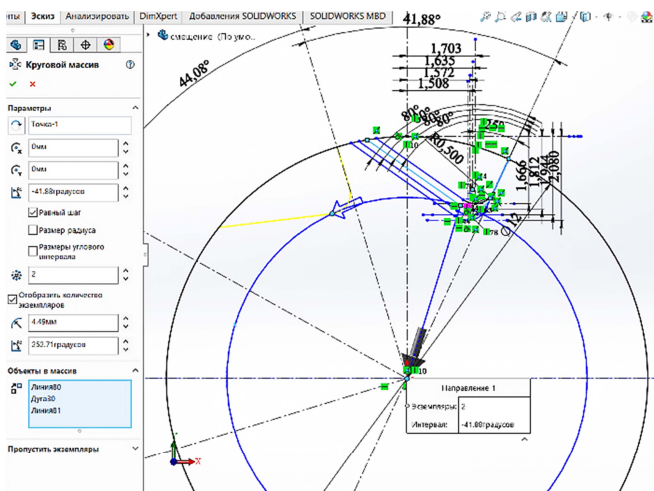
Поворот профиля канавки на заданный неравномерный окружной шаг
